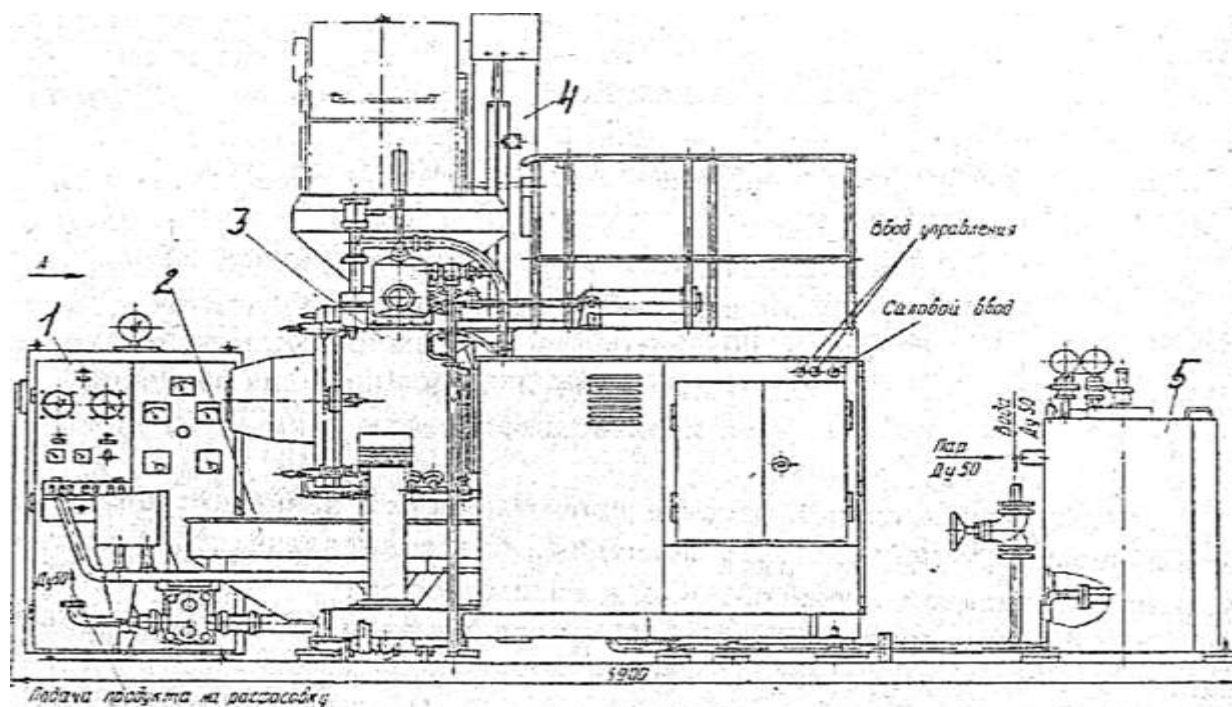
Общий вид агрегата марки В2-ОПН:
